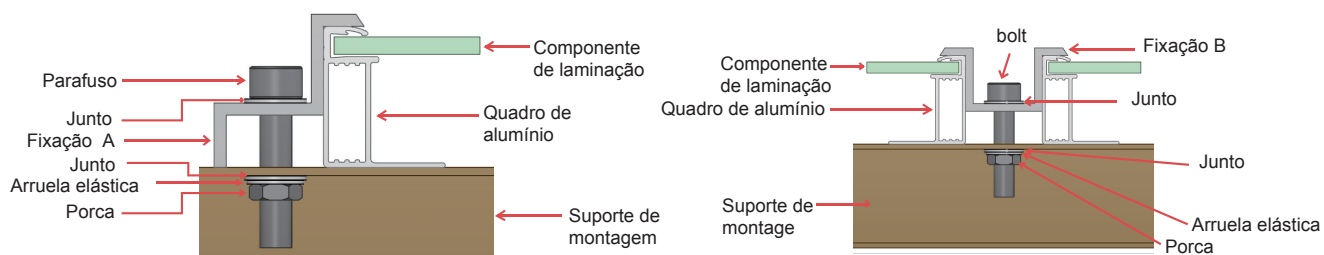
Diagrama de instalação dos fixações de montagem de componente de lado único
